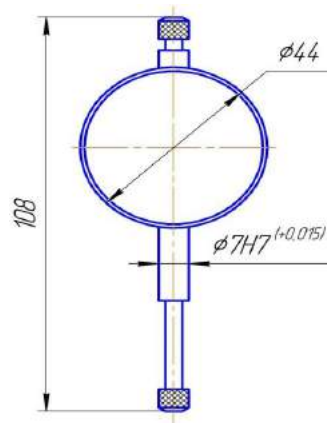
Габаритні розміри індикатора багатообертового моделі 2МИГ-1
